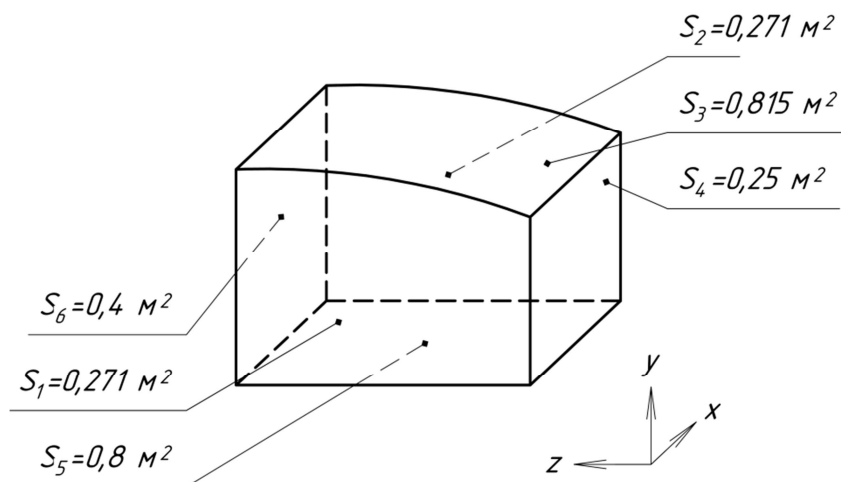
Схема расположения и обозначения панелированных элементов сварного отсека
